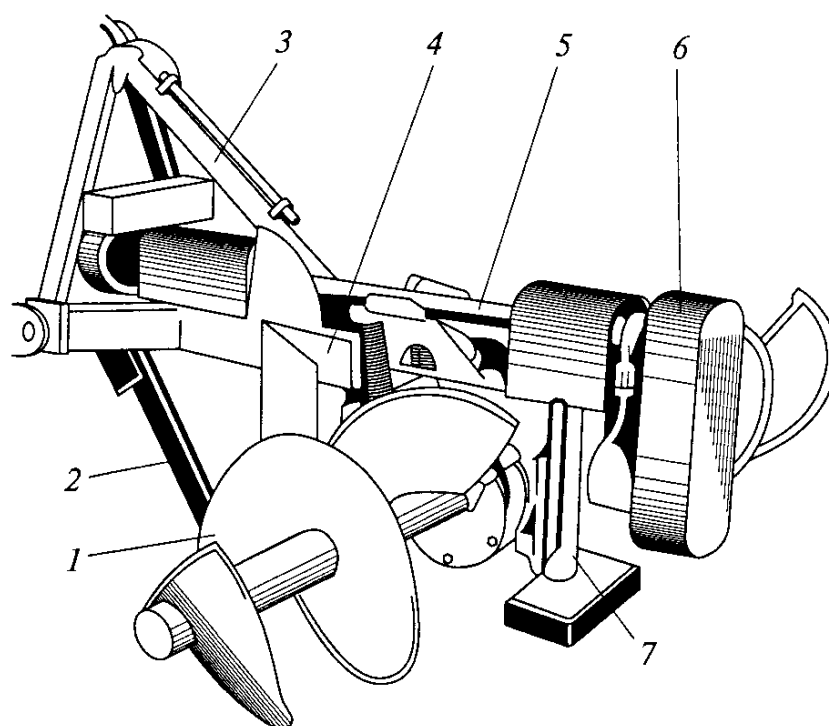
Плуг шнековый ПШ-1: 1 — шнековый барабан; 2 — черенковый нож; 3 — навеска; 4 — двухотвальный плужный корпус; 5 — карданный вал привода шнеков; 6 — кожух цепной передачи; 7 — стойка
